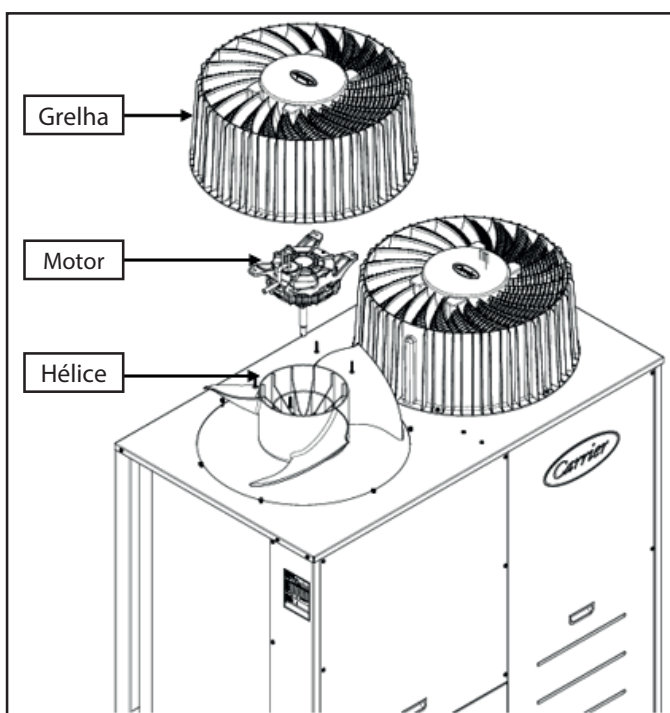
Vista explodida conjunto ventilador das unidades condensadora 38EXE e nova hélice Carrier
